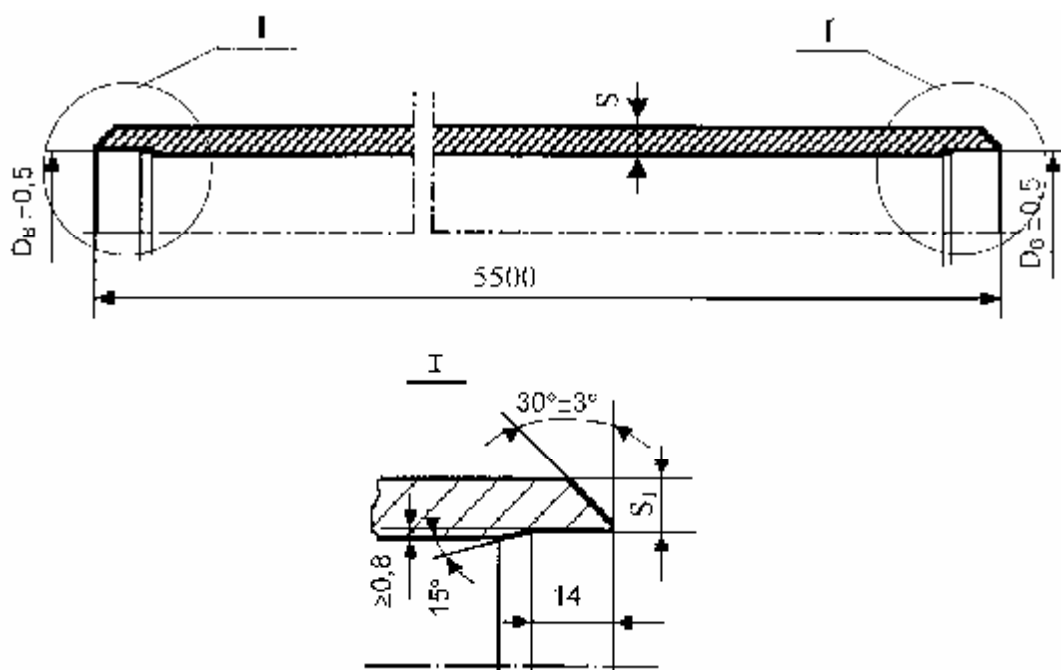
П13. Схема трубы с гладкими концами под сварку (тип Б)
